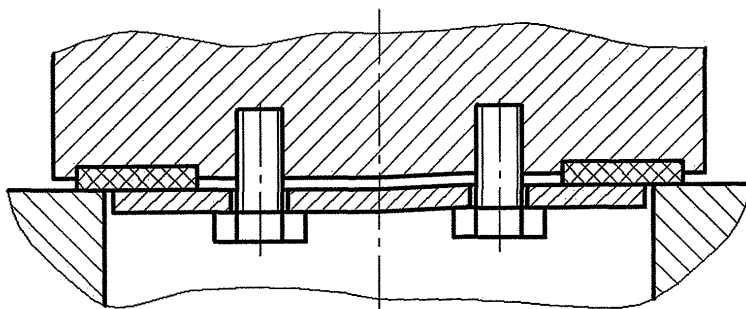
Крепление уплотнительного кольца тремя или четырьмя болтами
